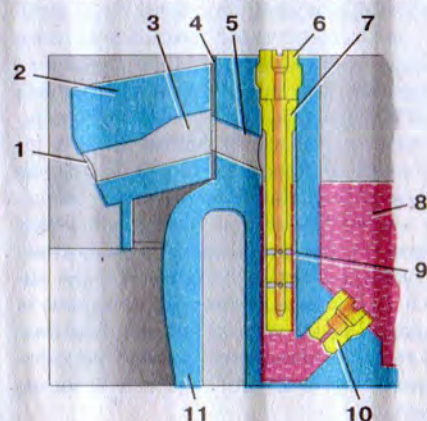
Схема главной дозирующей системы: 1 — выходное отверстие распылителя; 2 — малый диффузор; 3 — канал распылителя; 4 — уплотнительная прокладка; 5 — соединительный канал; 6 — главный воздушный жиклер; 7 — эмульсионная трубка; 8 — поплавковая камера; 9 — эмульсионный колодец; 10 — главный топливный жиклер; 11 — большой диффузор
